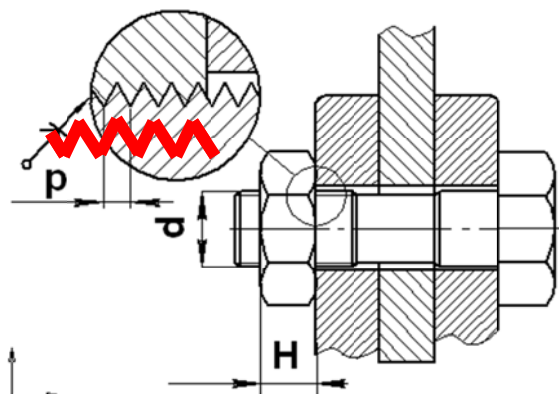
Стопорение резьбового соединения нанесением анаэробного клея в зазор резьбы болт-гайка
